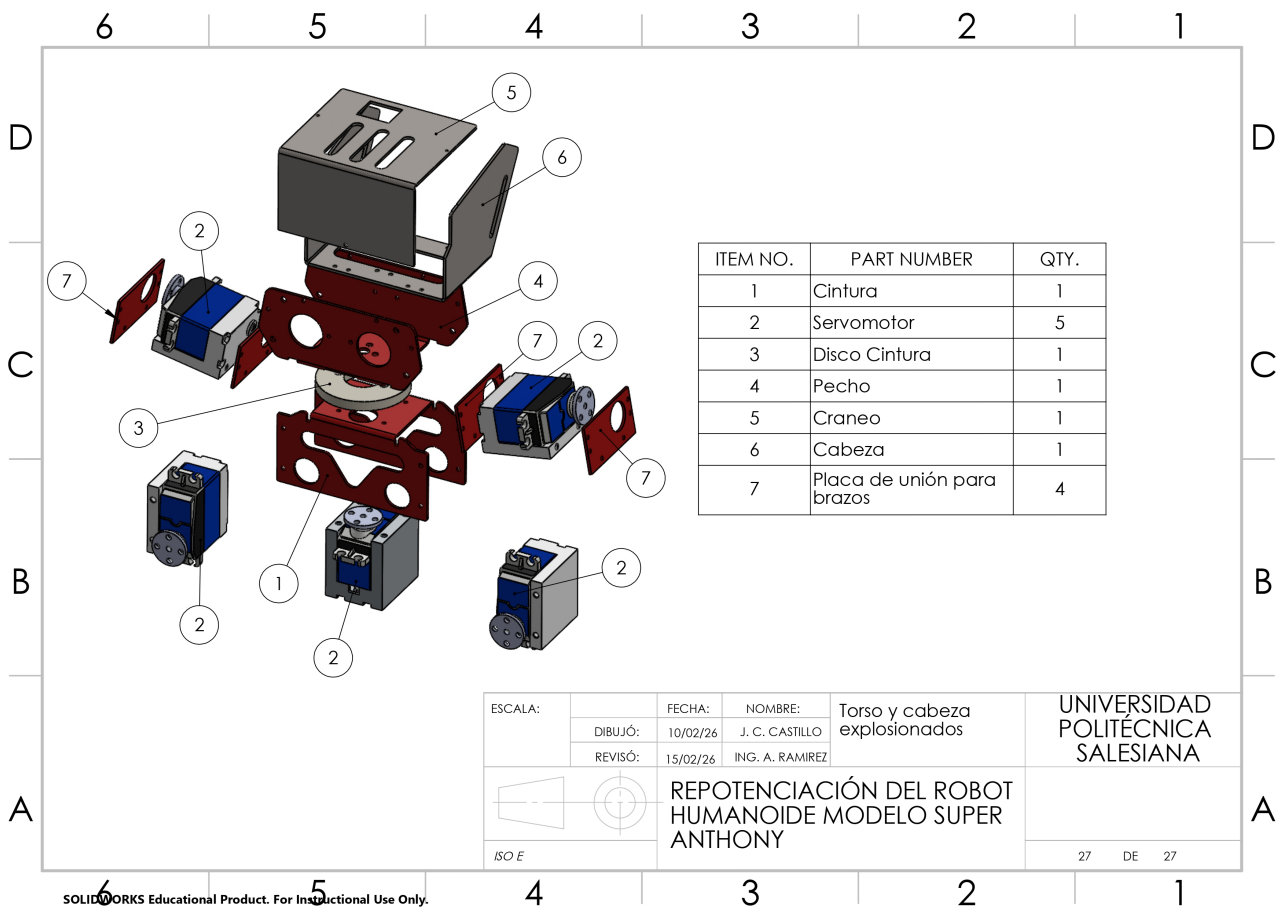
Lámina acotada de la vista explosionada del ensamblaje del torso y la cabeza del robot humanoide, por J. Castillo y B. Gualle, Solidworks
